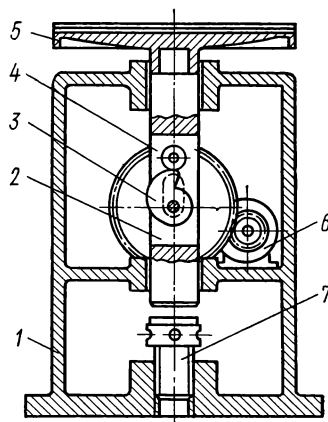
Установка для испытания приборов на устойчивость к тряске:
